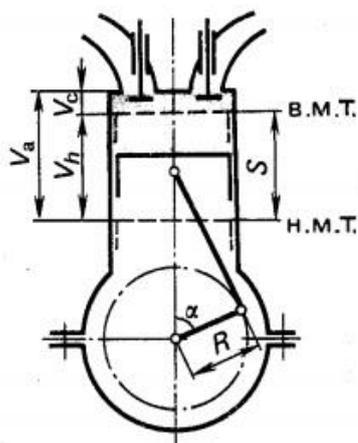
Схема одноцилиндрового четырехтактного двигателя
